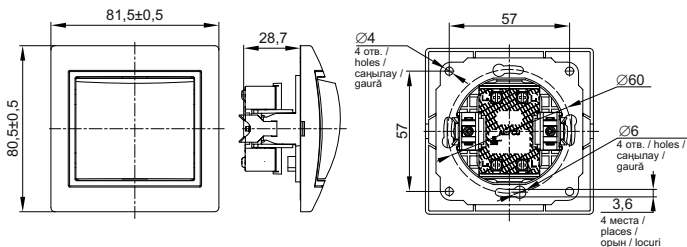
Габаритные и установочные размеры выключателя со степенью защиты IP20 и керамическим механизмом / Figure 3 – Overall and mounting dimensions of the switch with protection degree IP20 and ceramic mechanism / 3 сурет – IP20 қорғаныш дәрежесі және қыш механизмі бар ажыратқыштың габариттік және орнату өлшемдері / Figura 3 – Dimensiunile generale și de instalare ale comutatorului cu grad de protecție IP20 și mecanism ceramic
